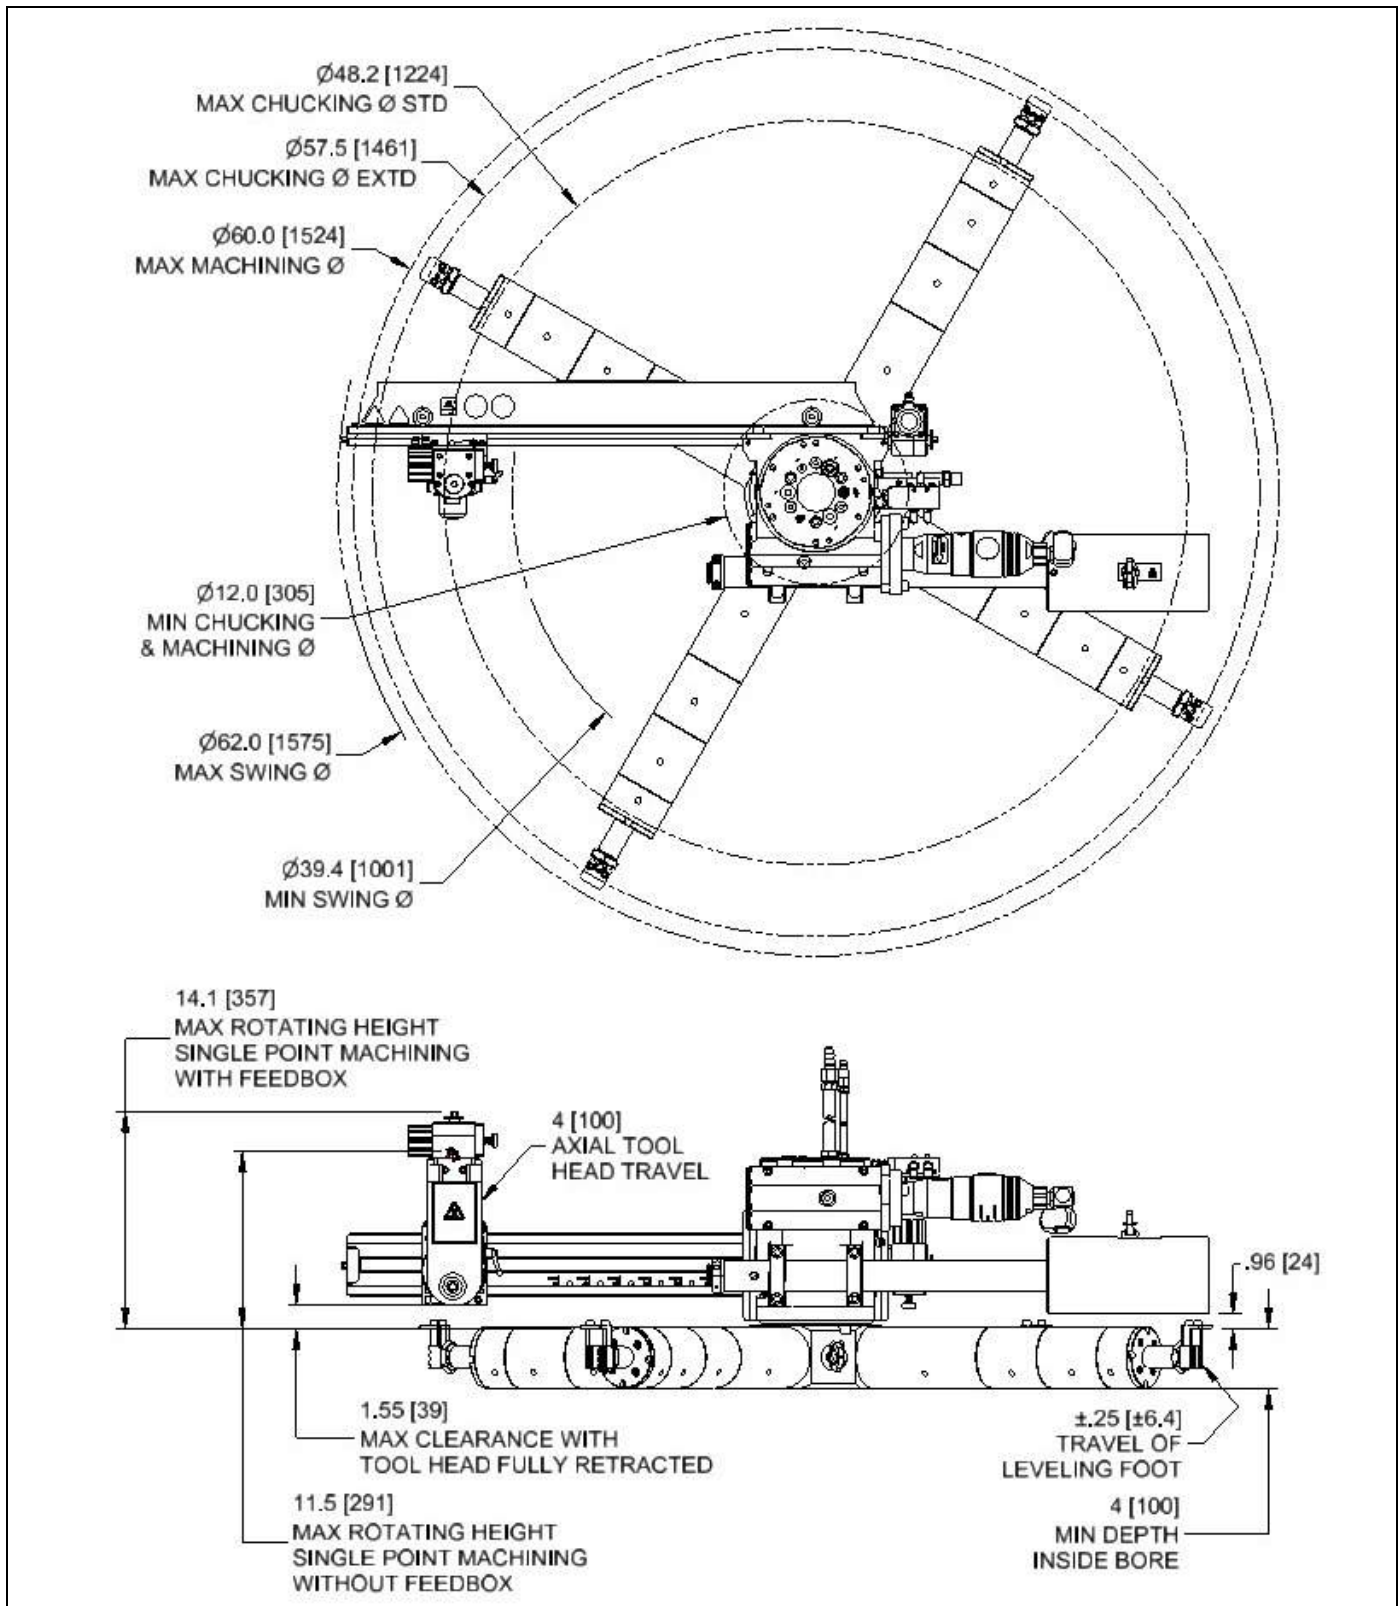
FF6300 DIMENSIONS DE L'ENSEMBLE MANDRIN DI
